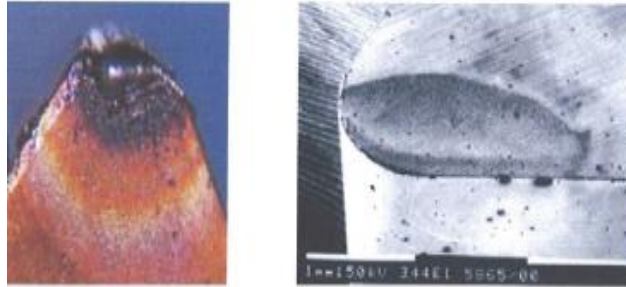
Cratère formé par usure par diffusion sur une plaquette carbure[14].
